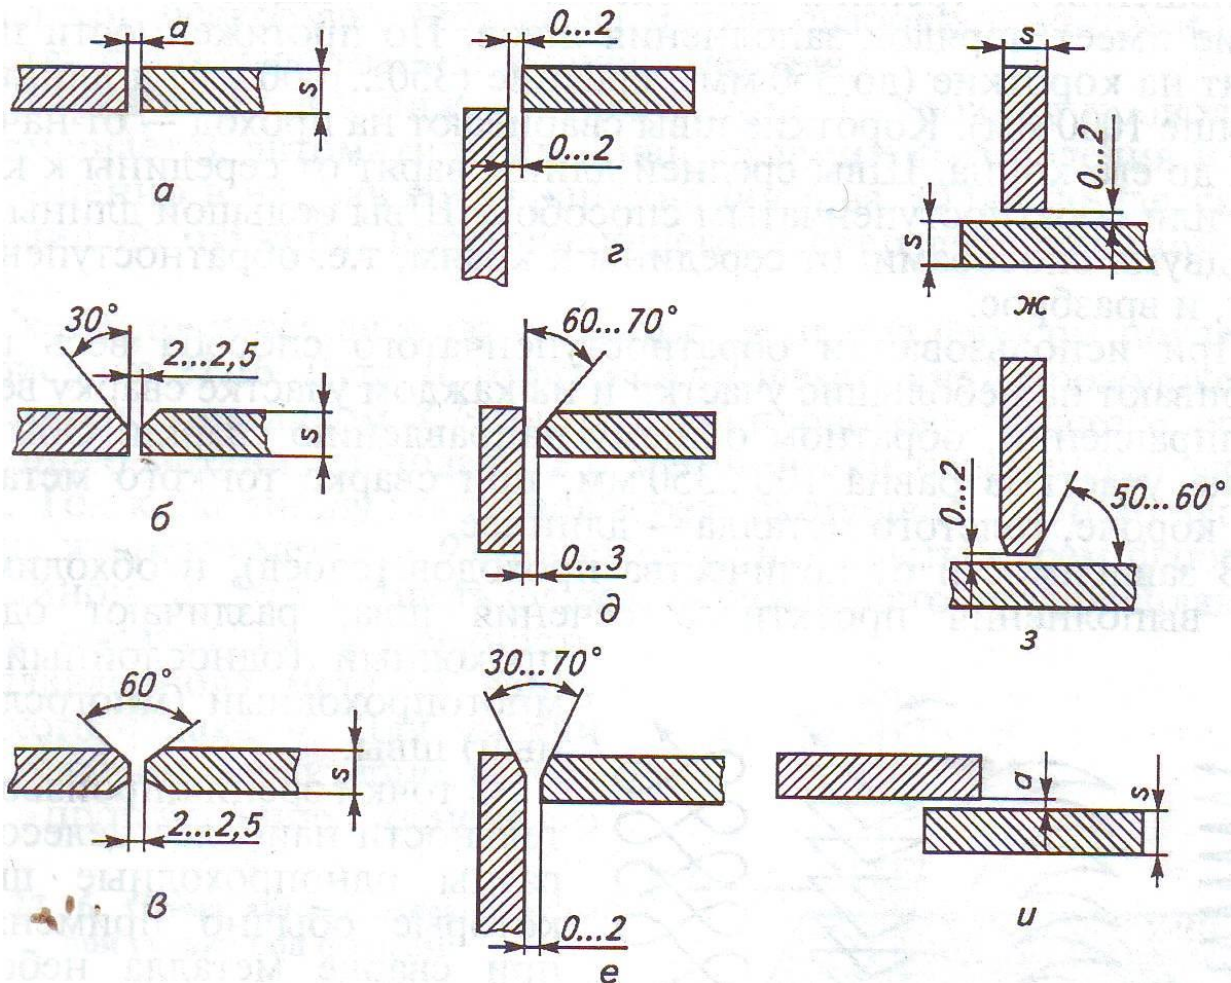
Рекомендуемые типы соединений для ручной дуговой сварки
